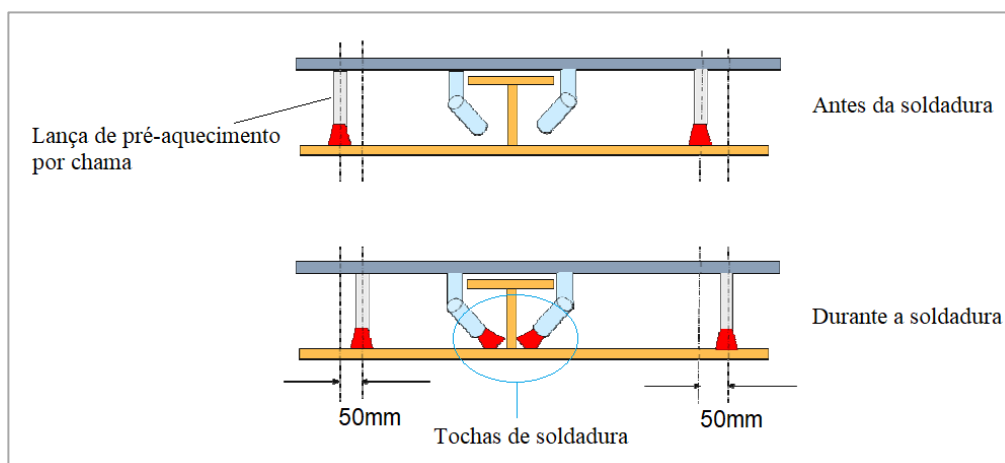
Aplicação de linhas de calor, antes e durante a soldadura - [35] Imagem adaptada
